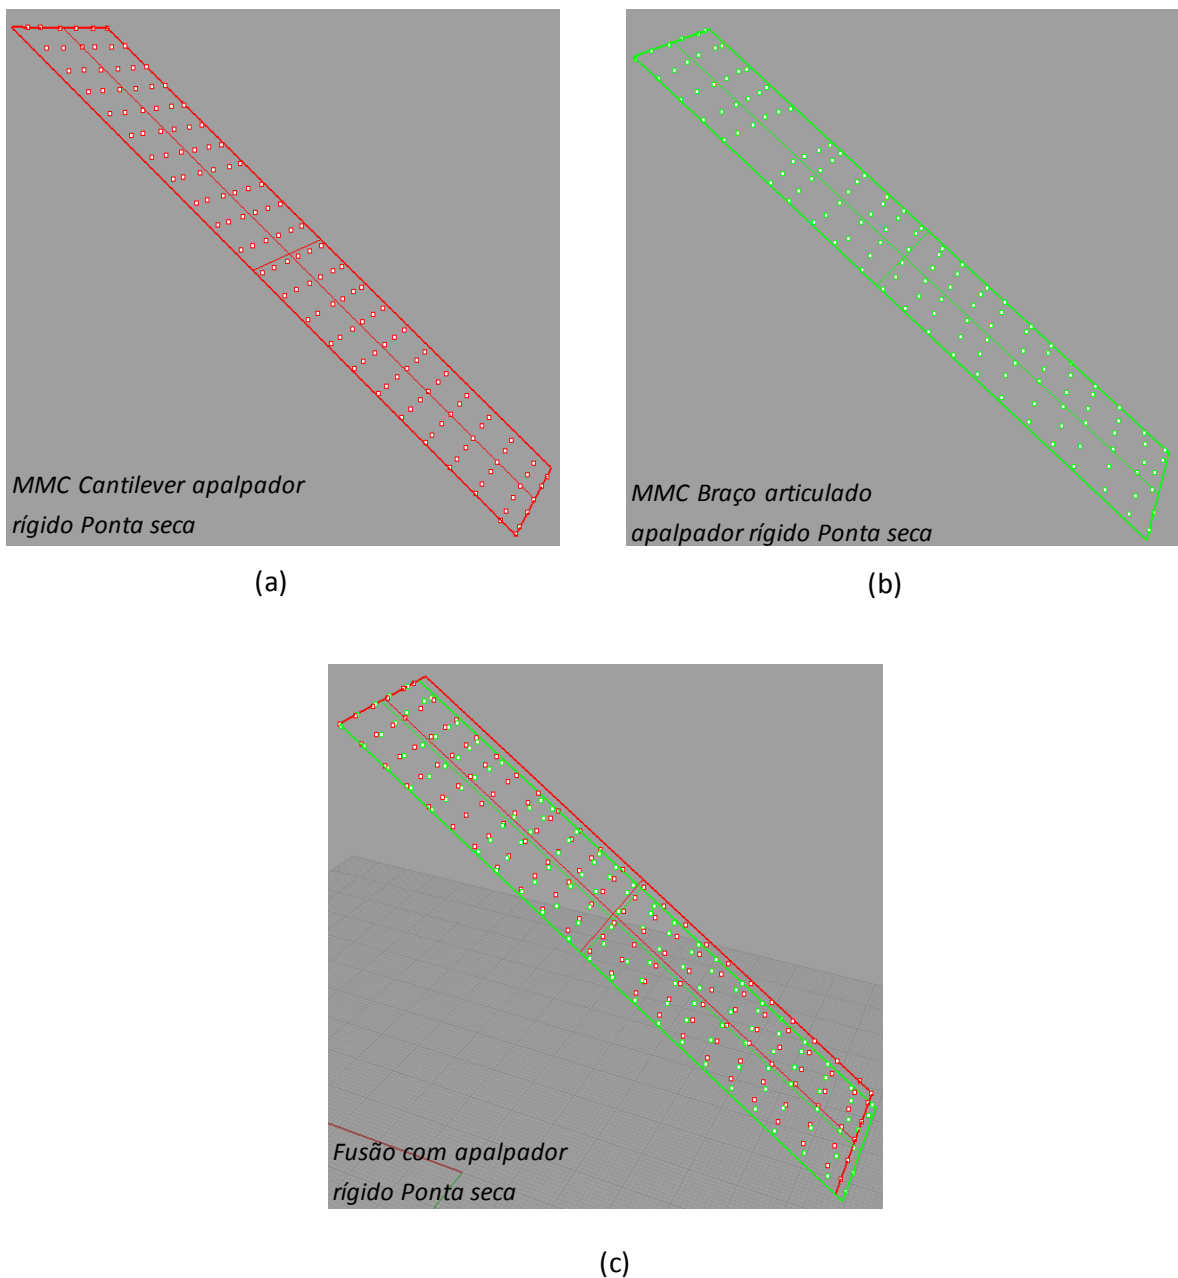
Plano Esquadro de Granito com apalpador rígido Ponta seca(a) MMC Cantilever, (b) MMC Braço Articulado, (c) Plano de Fusão.
